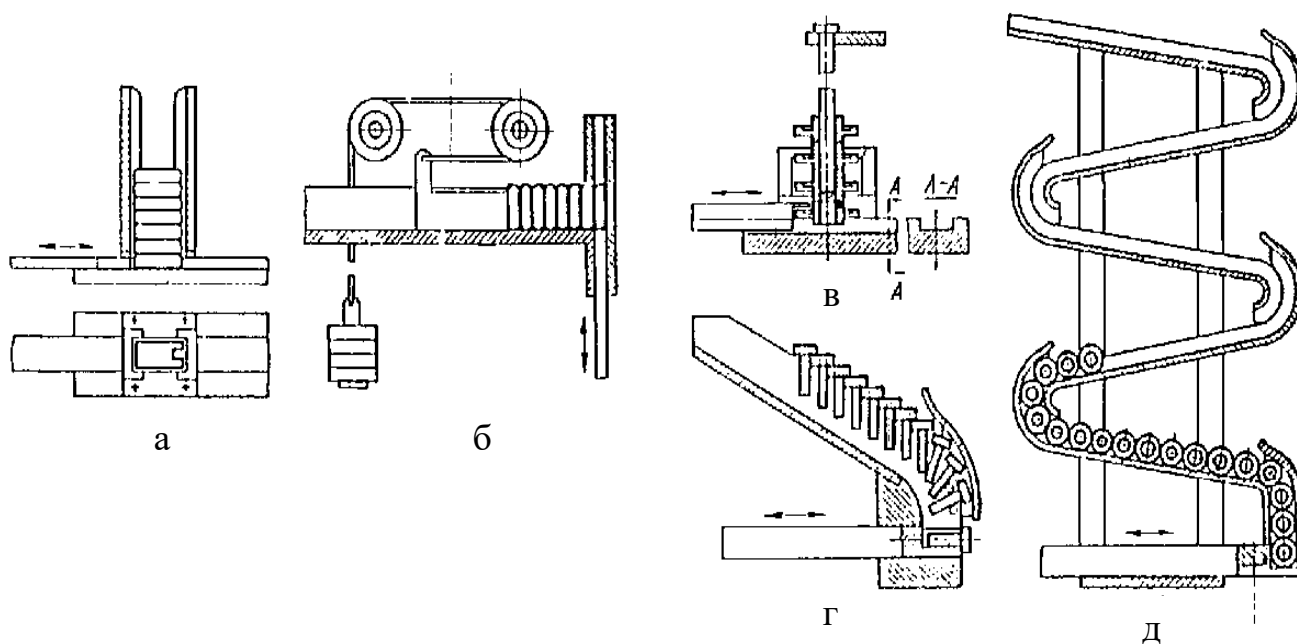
Магазины загрузочные устройства для заготовок, закладываемых штабелем в один ряд
